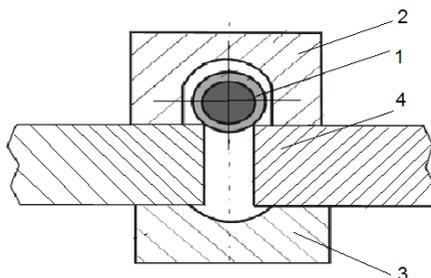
Схема сварки лежачим электродом: 1 – электрод; 2 – медный брусок; 3 – медная съемная подкладка; 4 – свариваемые пластины
